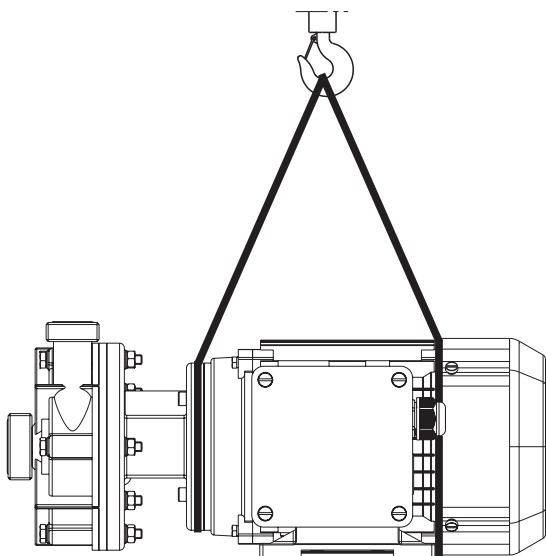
Hebezeug an der Blockpumpe befestigen (Prinzipbild)
